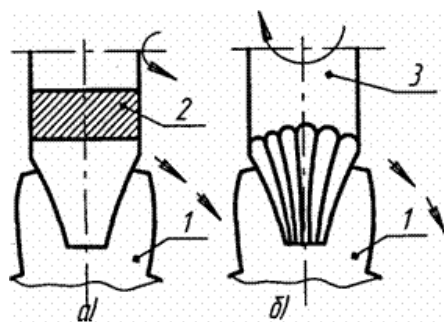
Схемы фрезерования цилиндрических колес методом копирования: а – дисковой фрезой; б – концевой фрезой;
